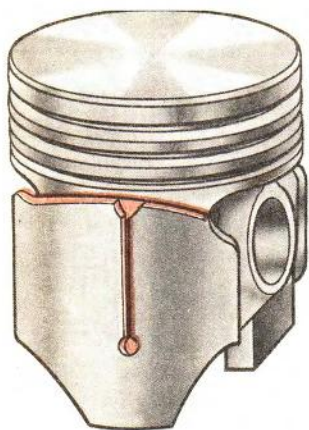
Поршень двигателя ЗМЗ-53-11.
